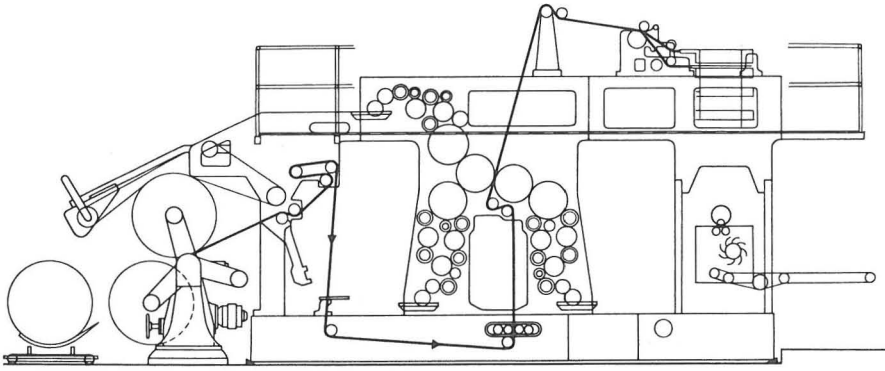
Rollen-Rotationsmaschine für indirekten Hochdruck von Wickelplatten in Parterreausführung
